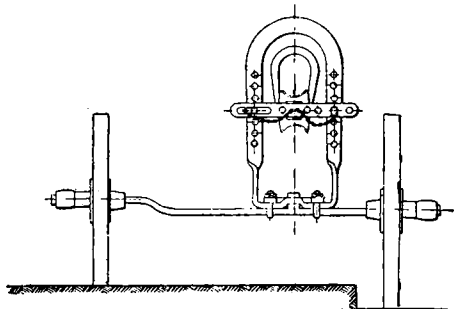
COTIGĂ cu osia dintr'o singură bucată.
